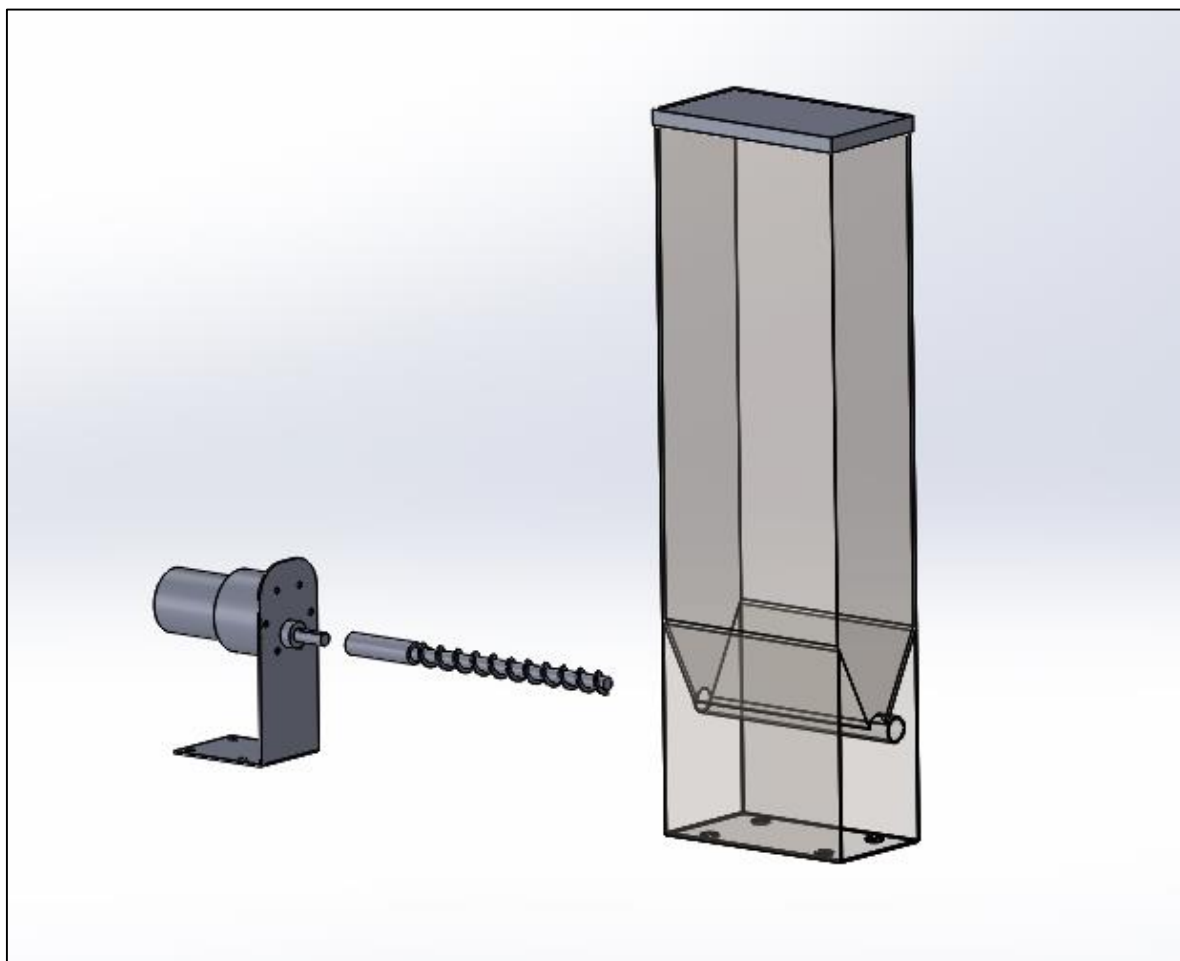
Vista 3D explodida do mecanismo de adição de sabor.
